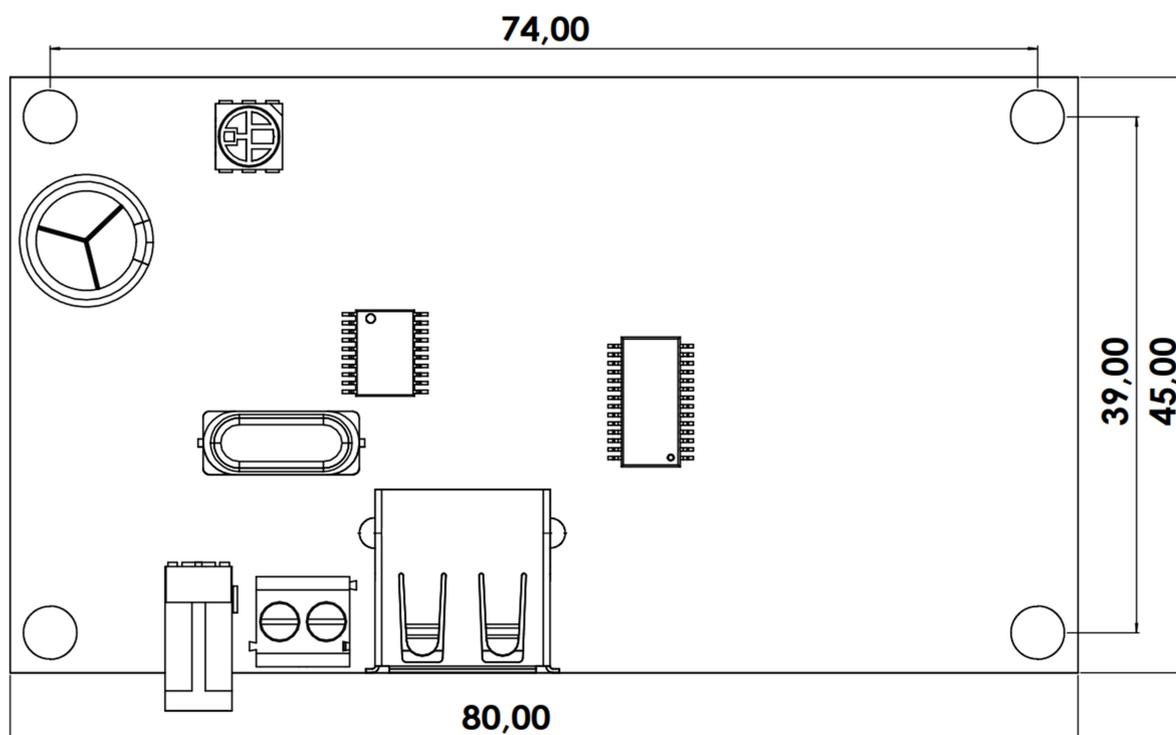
Габаритные размеры модуля RI-PWM1
